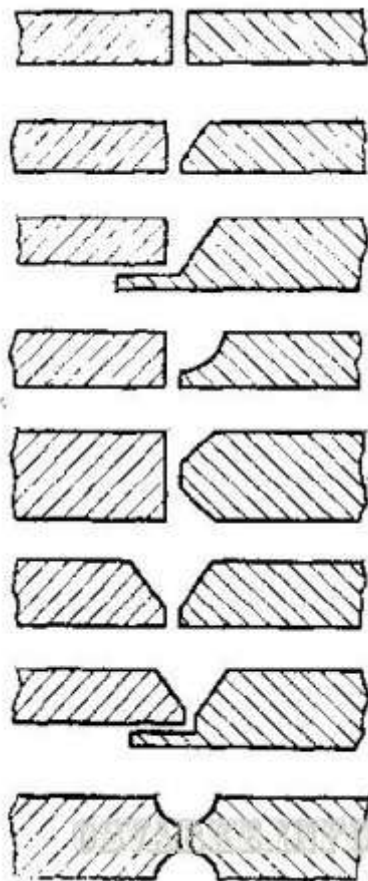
Форма подготовленных кромок под сварку для стыковых соединений.
